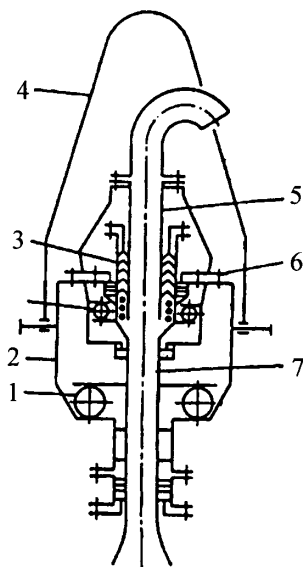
Вертлюг: 1 – подшипники; 2 – корпус; 3 – сальники; 4 – штроп; 5 – напорная труба; 6 – крышка корпуса; 7 – стол
